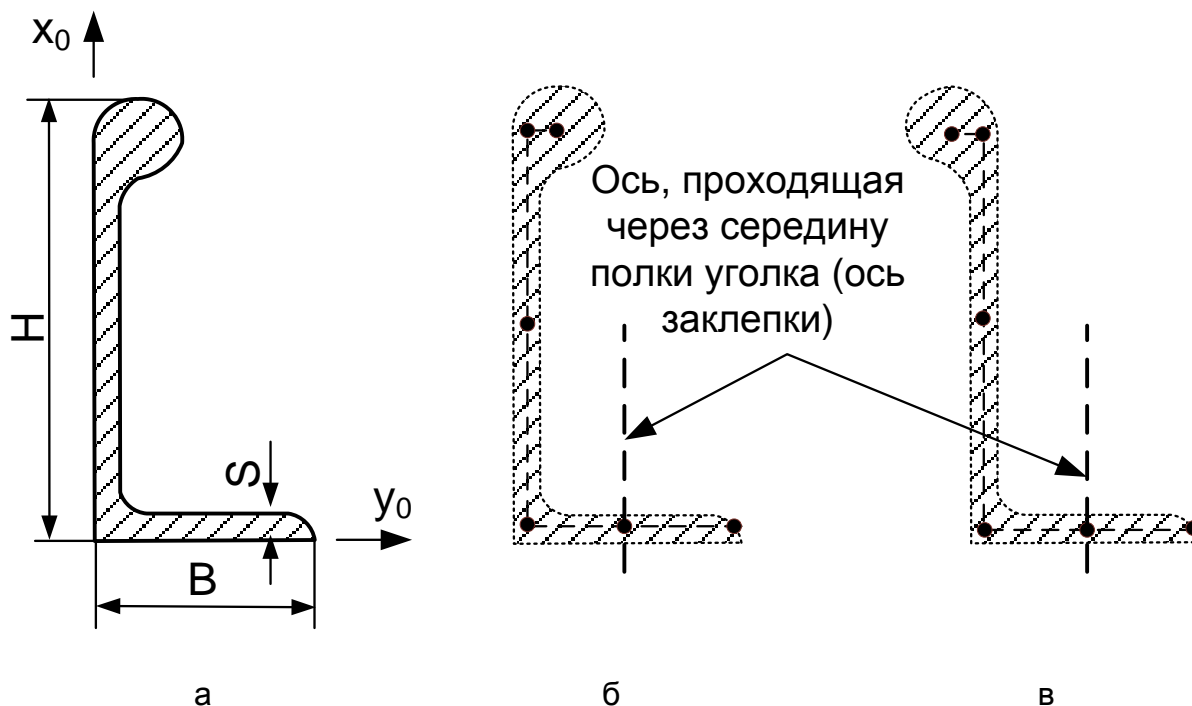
Поперечное сечение: а – бульбоугольник типа ПР 102; б – дискретное сечение бульбоугольника типа ПР 102; в – дискретное сечение бульбоугольника с внешней бульбой
